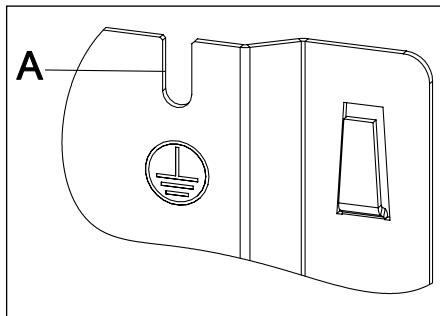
Collegamento equipotenziale di protezione / Messa a terra
